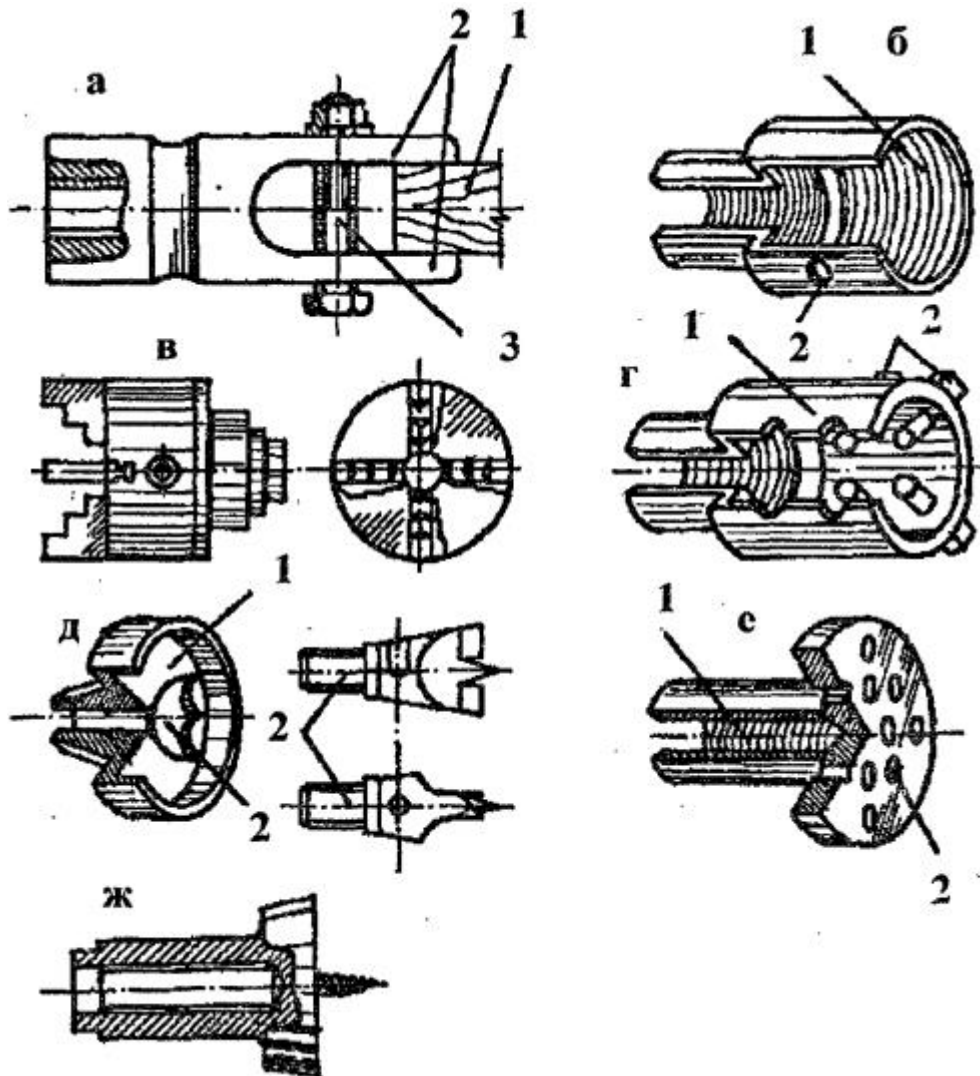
Приспособления для закрепления и обработки заготовок на станке:
